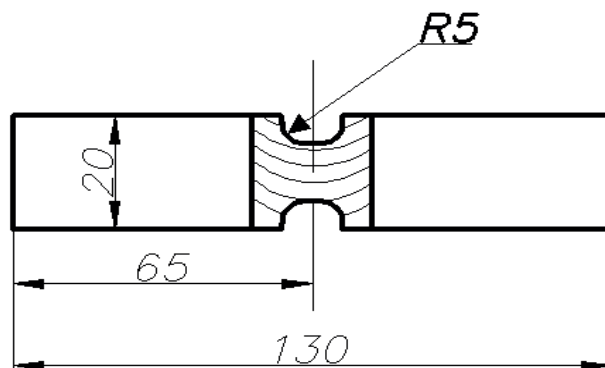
Образец для определения прочности металла шва, выполненного СТП
